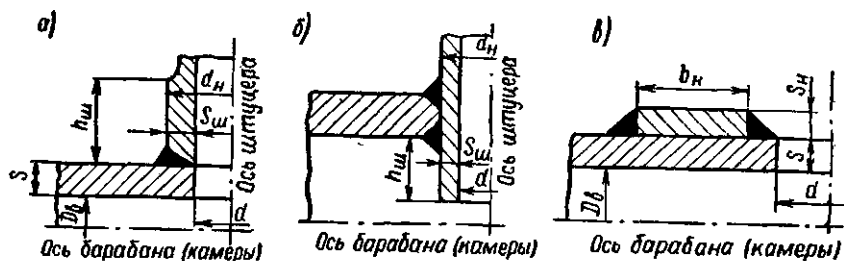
Укрепление отверстий: а — при помощи приварного штуцера; б — при помощи приварного штуцера, не испытывающего давления; в — при помощи накладки.
